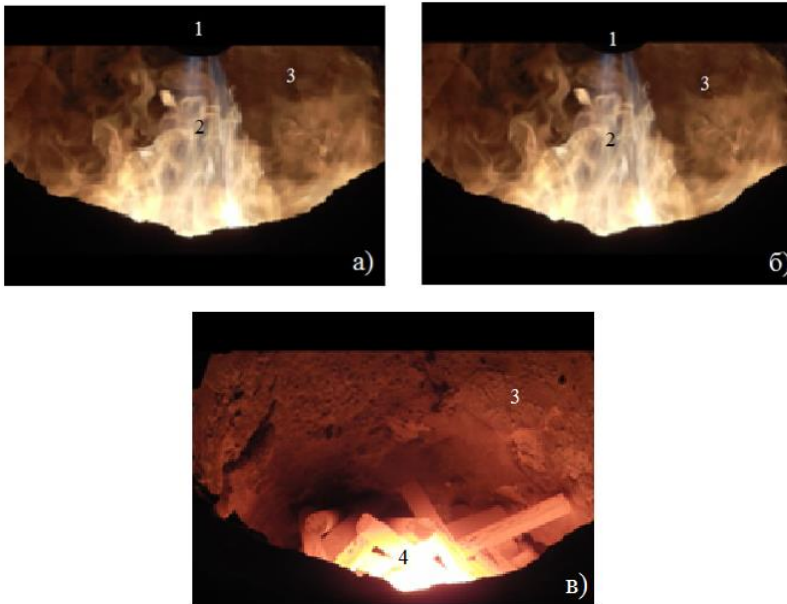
Динаміка нагріву металевому брухту пропан-бутановим факелом: 1- головка паливно-кисневої фурми; 2- сформований пропан-бутановий факел; 3- футеровка конвертера; 4 – нагрітий металевий брухт
